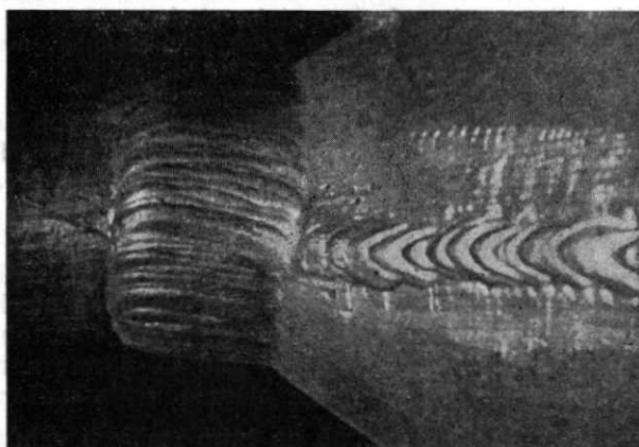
Sváření kolmo 10 mm silného olověného plechu vzhůru ve dvou vrstvách hořákem vodíko-kyslíkovým.
